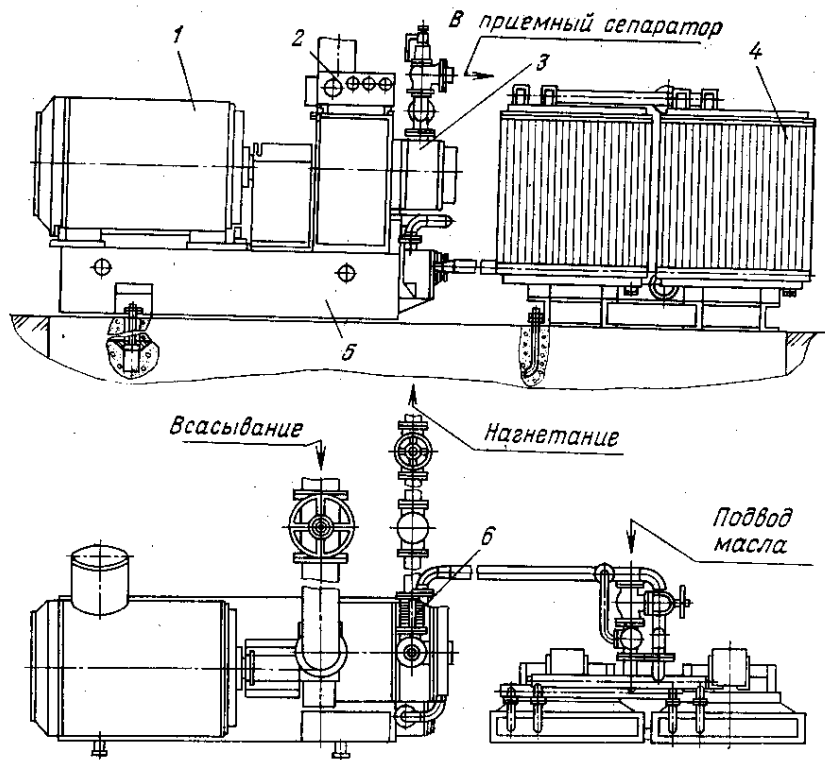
Компрессорная установка 7ВКГ-50/7:
